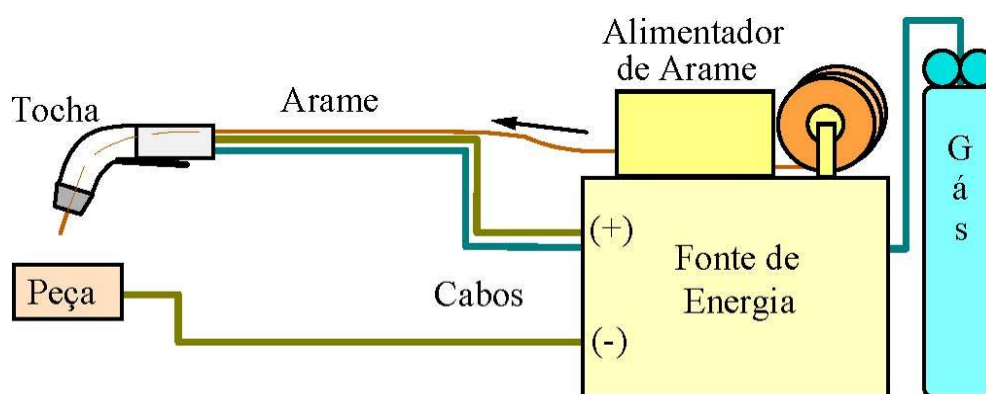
Equipamento para a soldagem GMAW (Modenesi e Marques, 2006).
